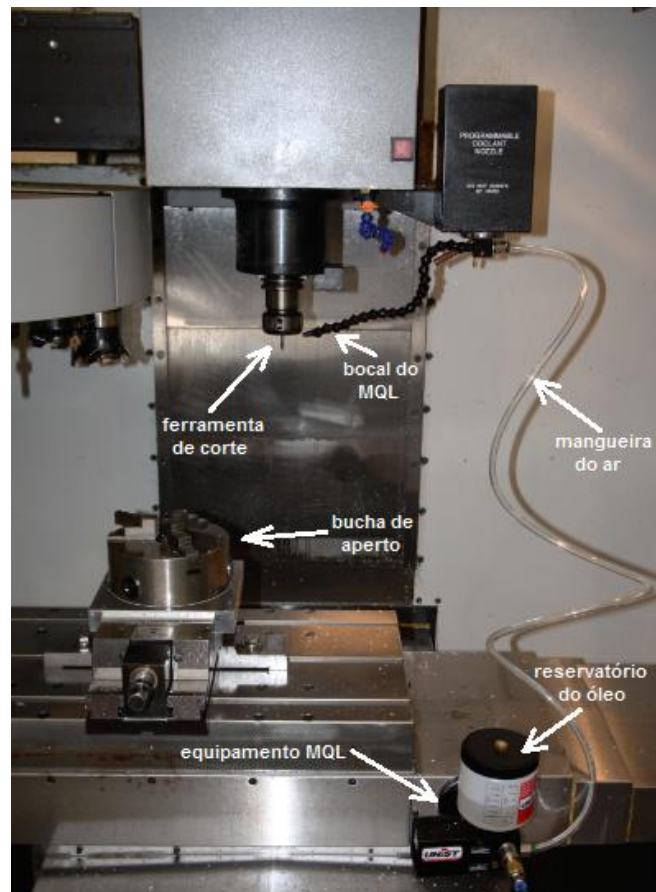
Coolubricator JR™ instalado no centro de maquinagem CNC.
